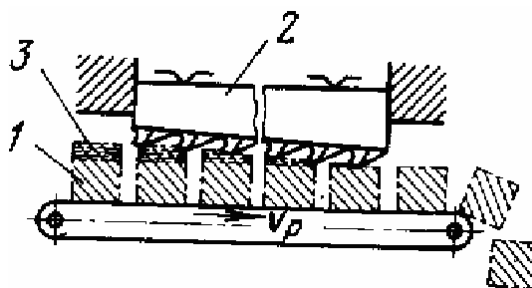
Схемы обработки наружных поверхностей на протяжных станках:
